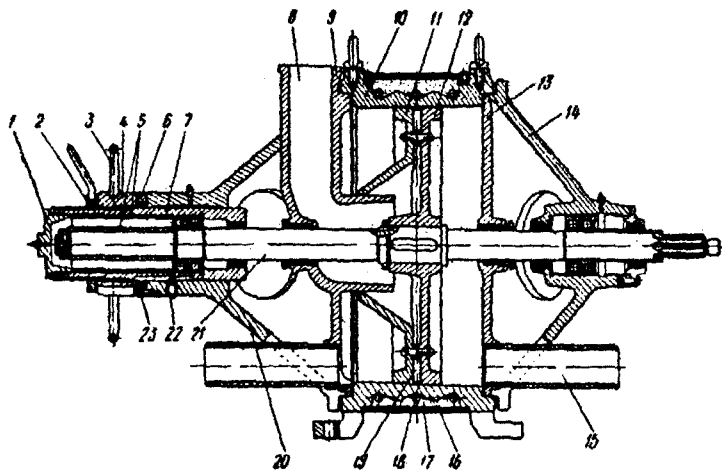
Одноконусный гомогенизатор: 1 – крышка подшипника; 2 – стопорная гайка; 3 – штурвал; 4 – регулировочная гайка; 5 – втулки; 6 – замок; 7 – стакан; 8 – приемный канал; 9 и 13 – крышки корпуса; 10 – корпус; 11 и 12 – диски ротора; 14 и 20 – кронштейны; 15 – патрубки; 16 – кожух; 17 – теплоизоляция; 18 – электронагреватели; 19 – лопасти; 21 – вал; 22 – стопор; 23 – винт
